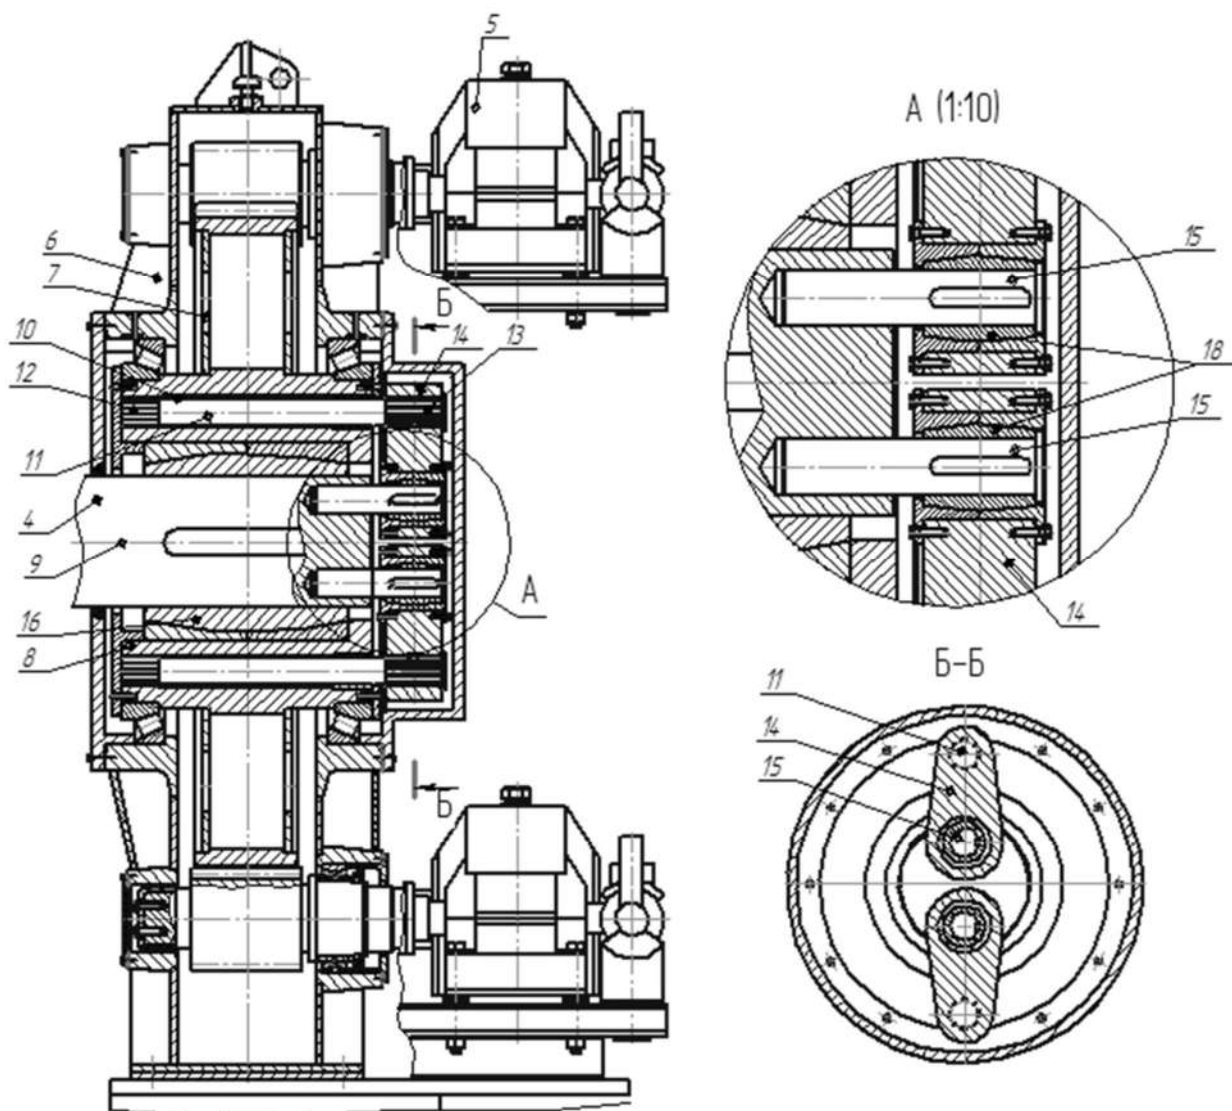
Перетини тихохідного редуктора привода повороту конвертора
